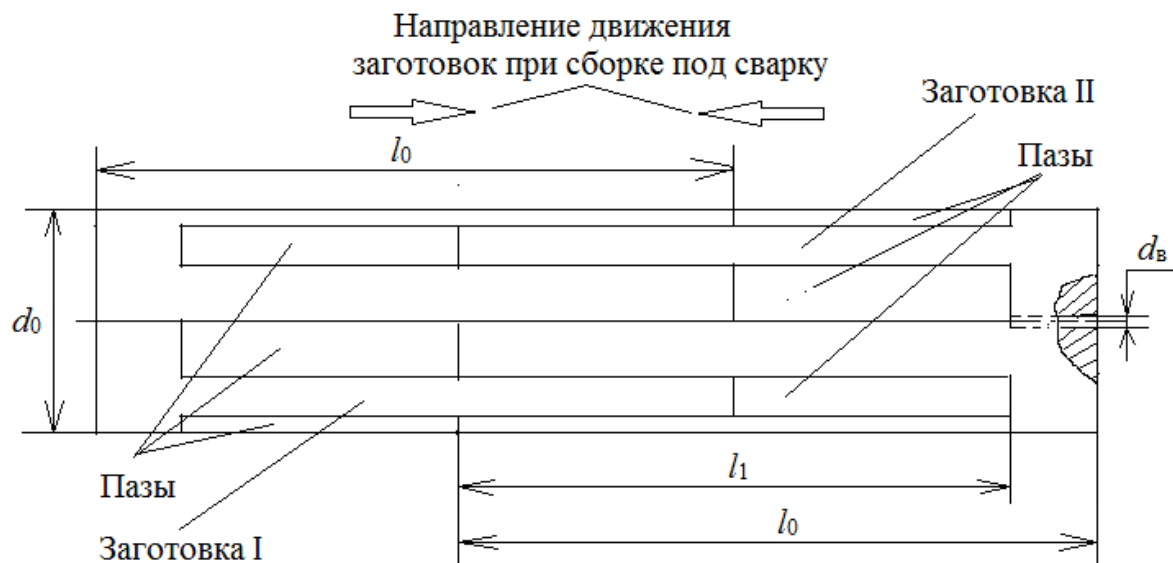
Сборки заготовок под сварку; d_0 — технологическое отверстие для вакуумирования внутренней полости заготовок при сварке
